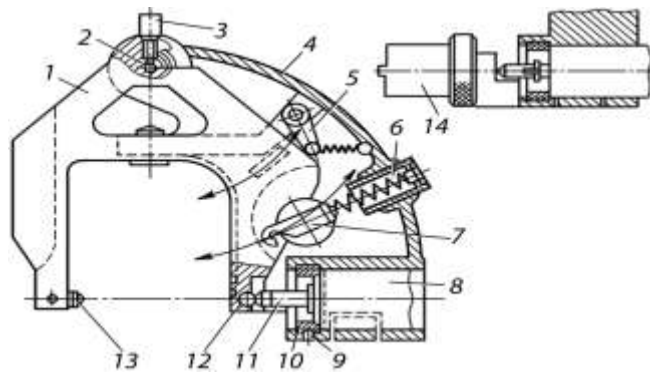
Пристосування для вимірювання внутрішніх розмірів
